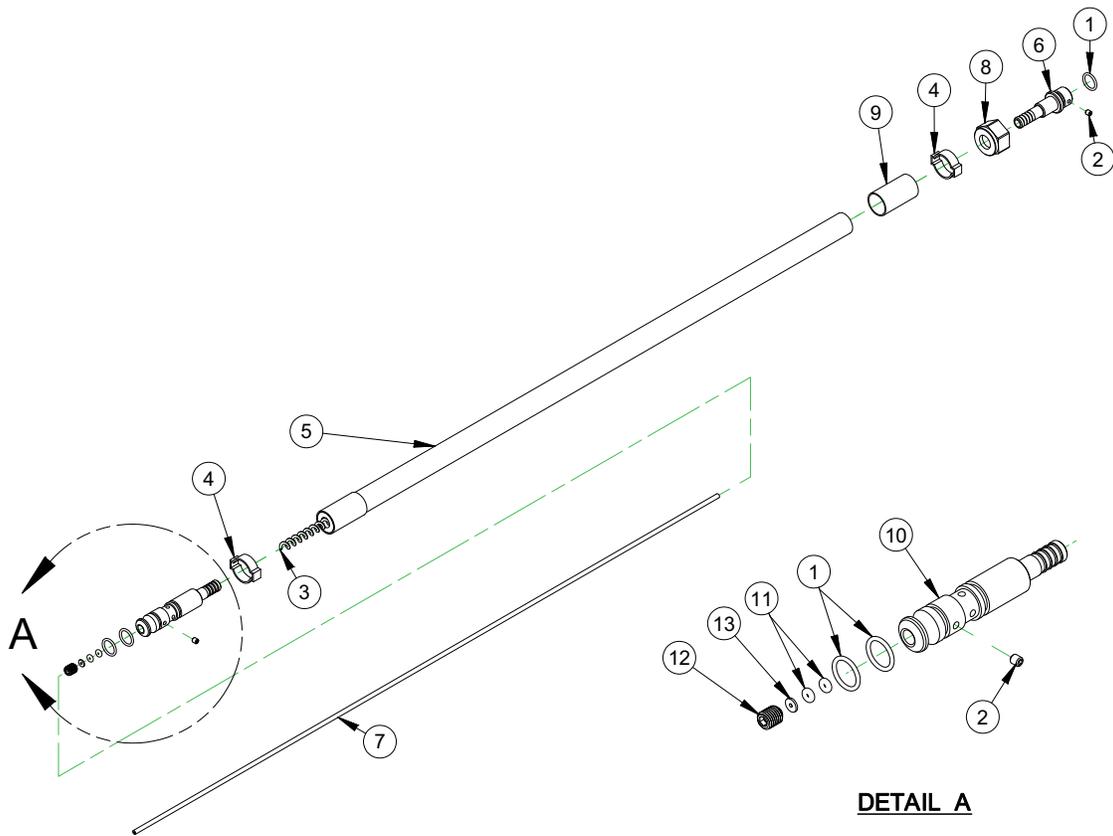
ENSEMBLE EXTENSION TORCHE 76 MM ET 152 MM (RÉF. 82155)
